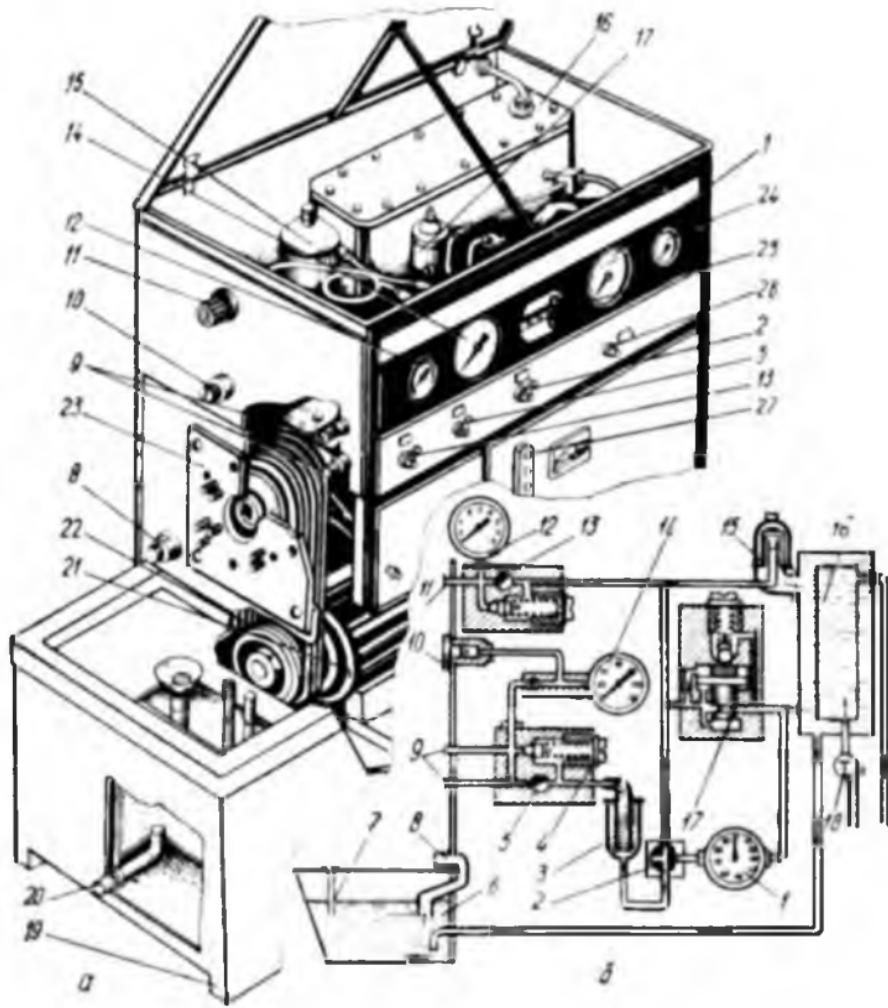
Стенд КИ-4200 для испытания гидроприводов:
